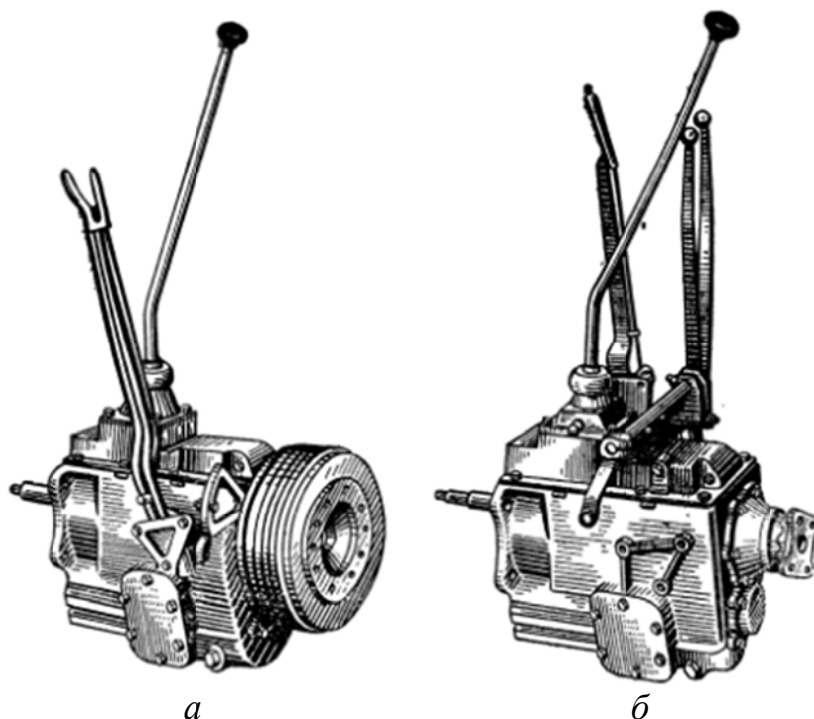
Коробки передач автомобилей ЗИЛ:
